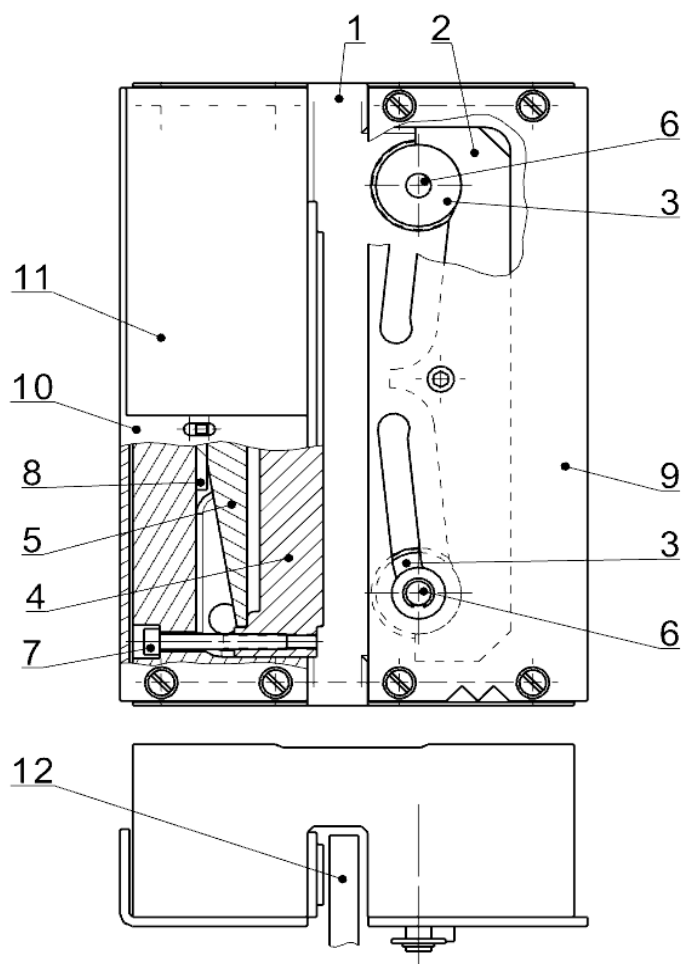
Общий вид ловителя: 1 – корпус; 2 – основание; 3 – ролики; 4 – тормозная колодка; 5 – пружина; 6 – оси; 7 – винты; 8 – регулировочные прокладки; 9 – направляющая пластина; 10 – пластина; 11 – табличка-пломба; 12 – направляющая
